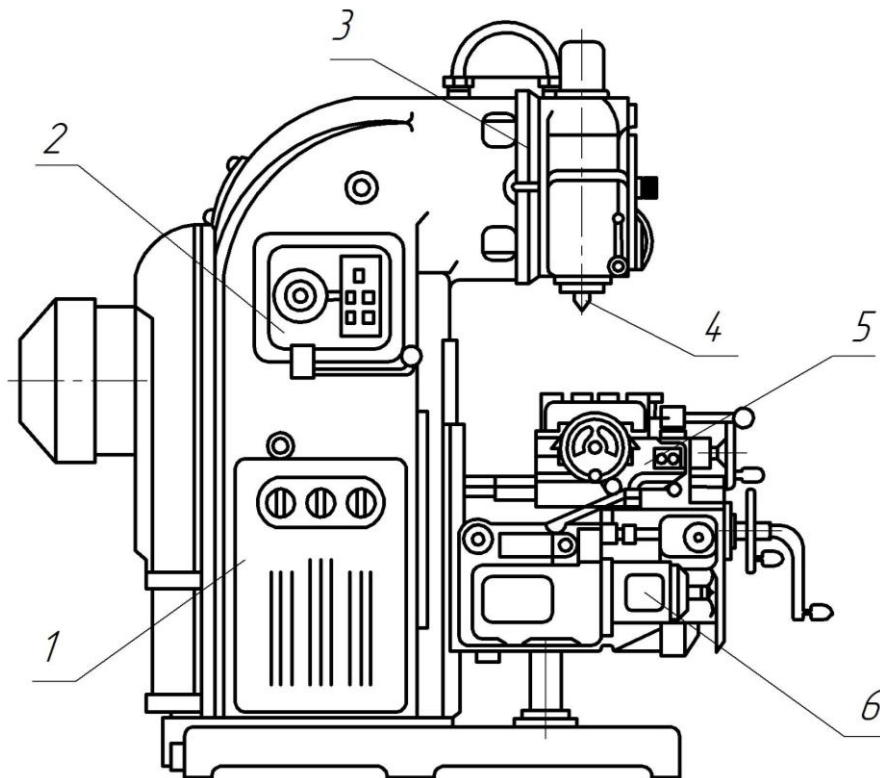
Загальний вигляд вертикально-фрезерного верстата
